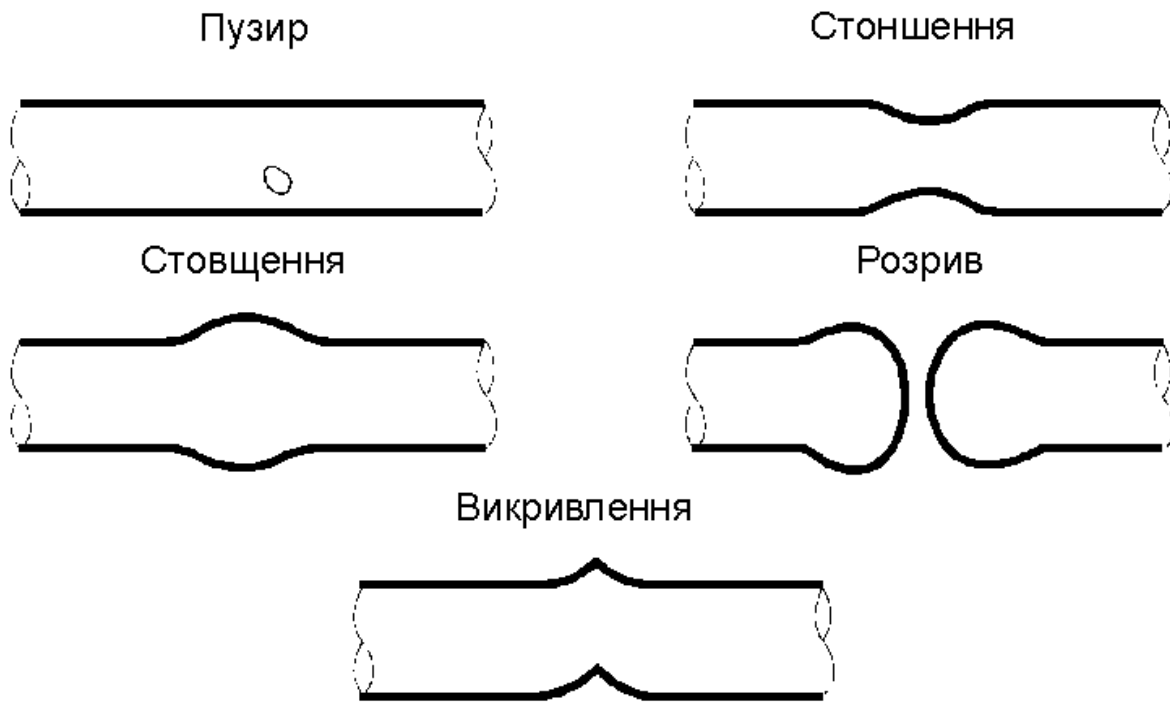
Дефекти зварювання ОВ
